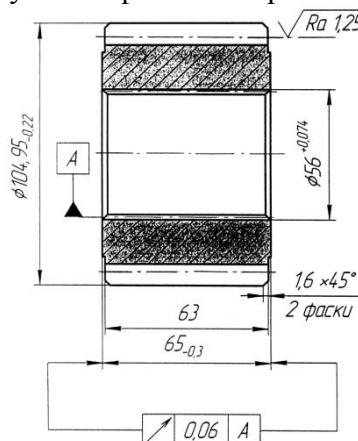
Ведущая цилиндрическая шестерня планетарной передачи
